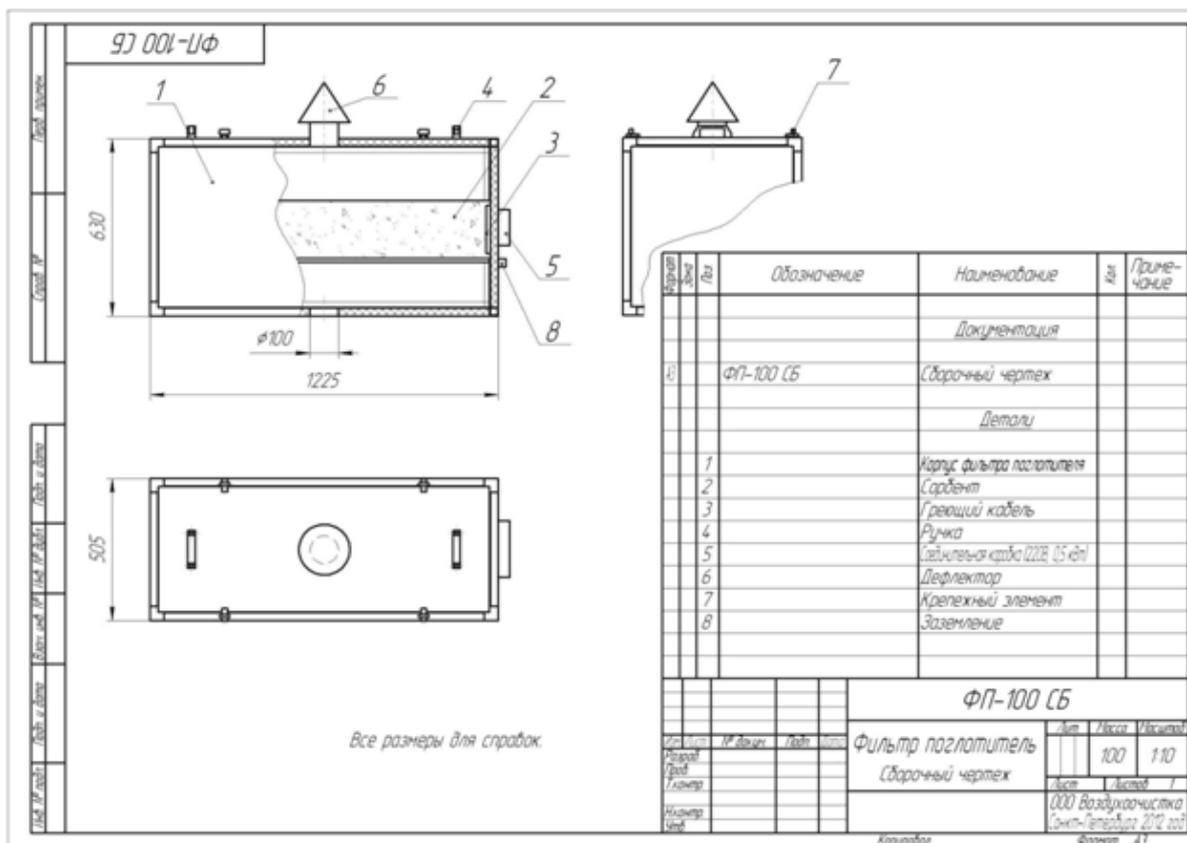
Сборочный чертёж фильтра поглотителя ФП-100 СБ
